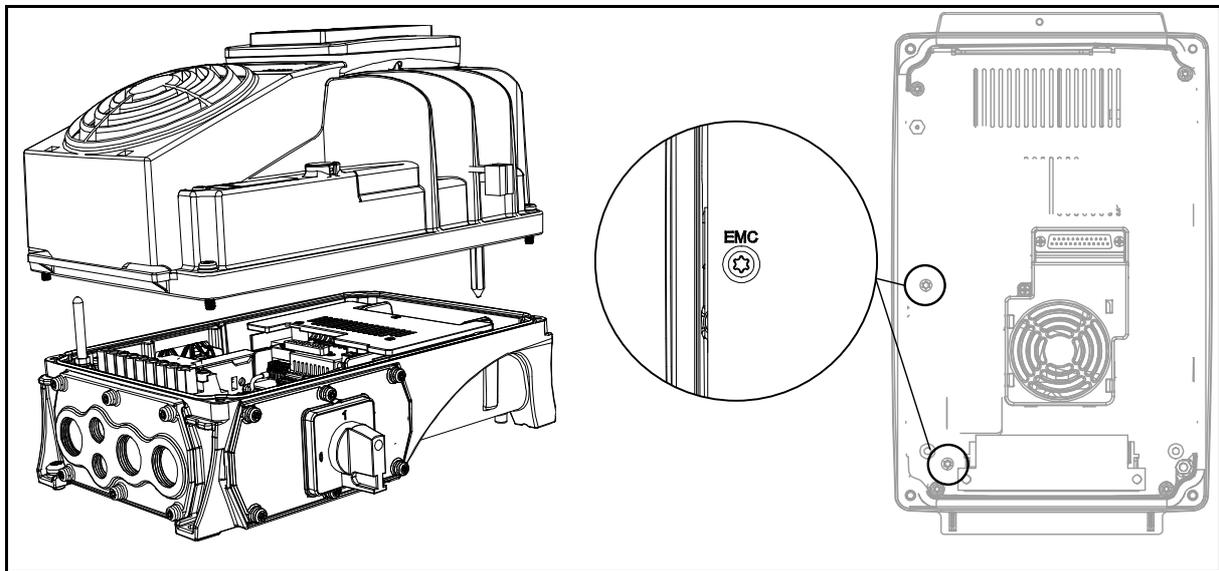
Position der EMV-Schrauben, Baugröße MM4.
